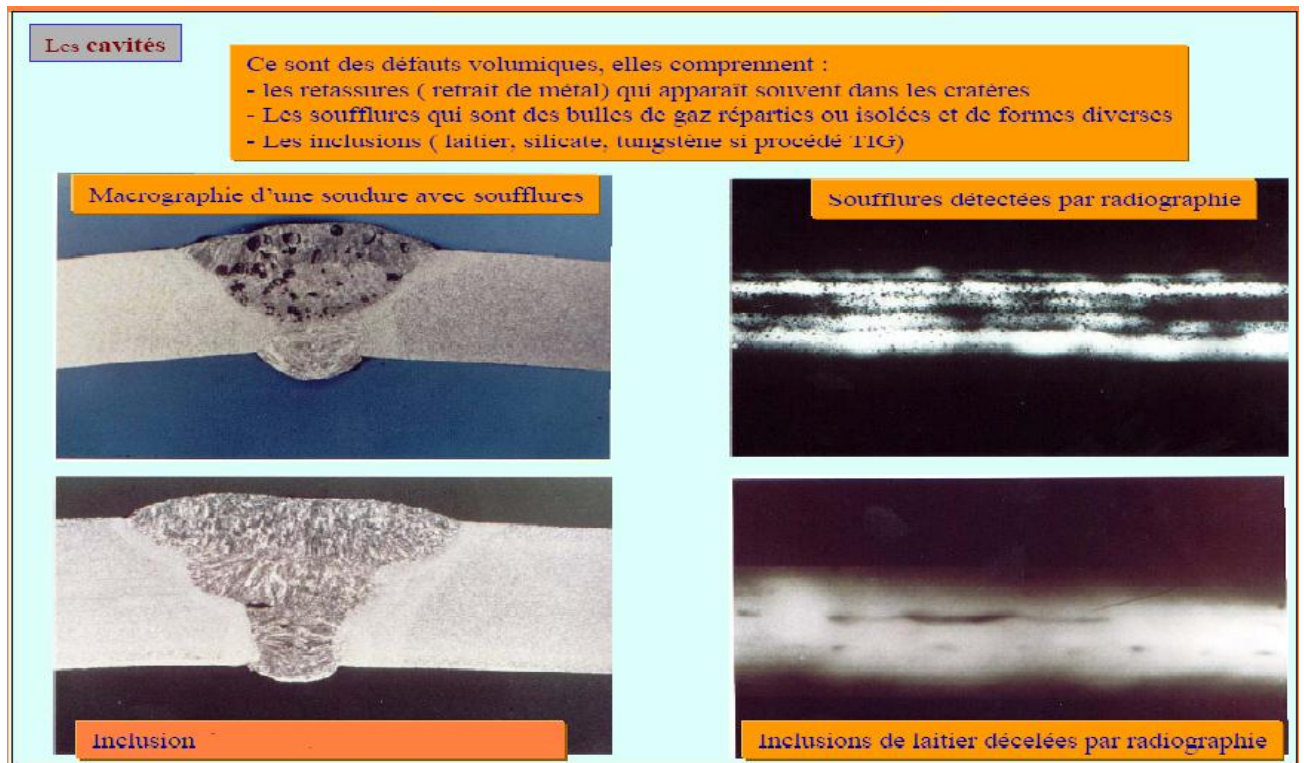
Défauts de cavités de soudure décelés par macrographie et radiographie
